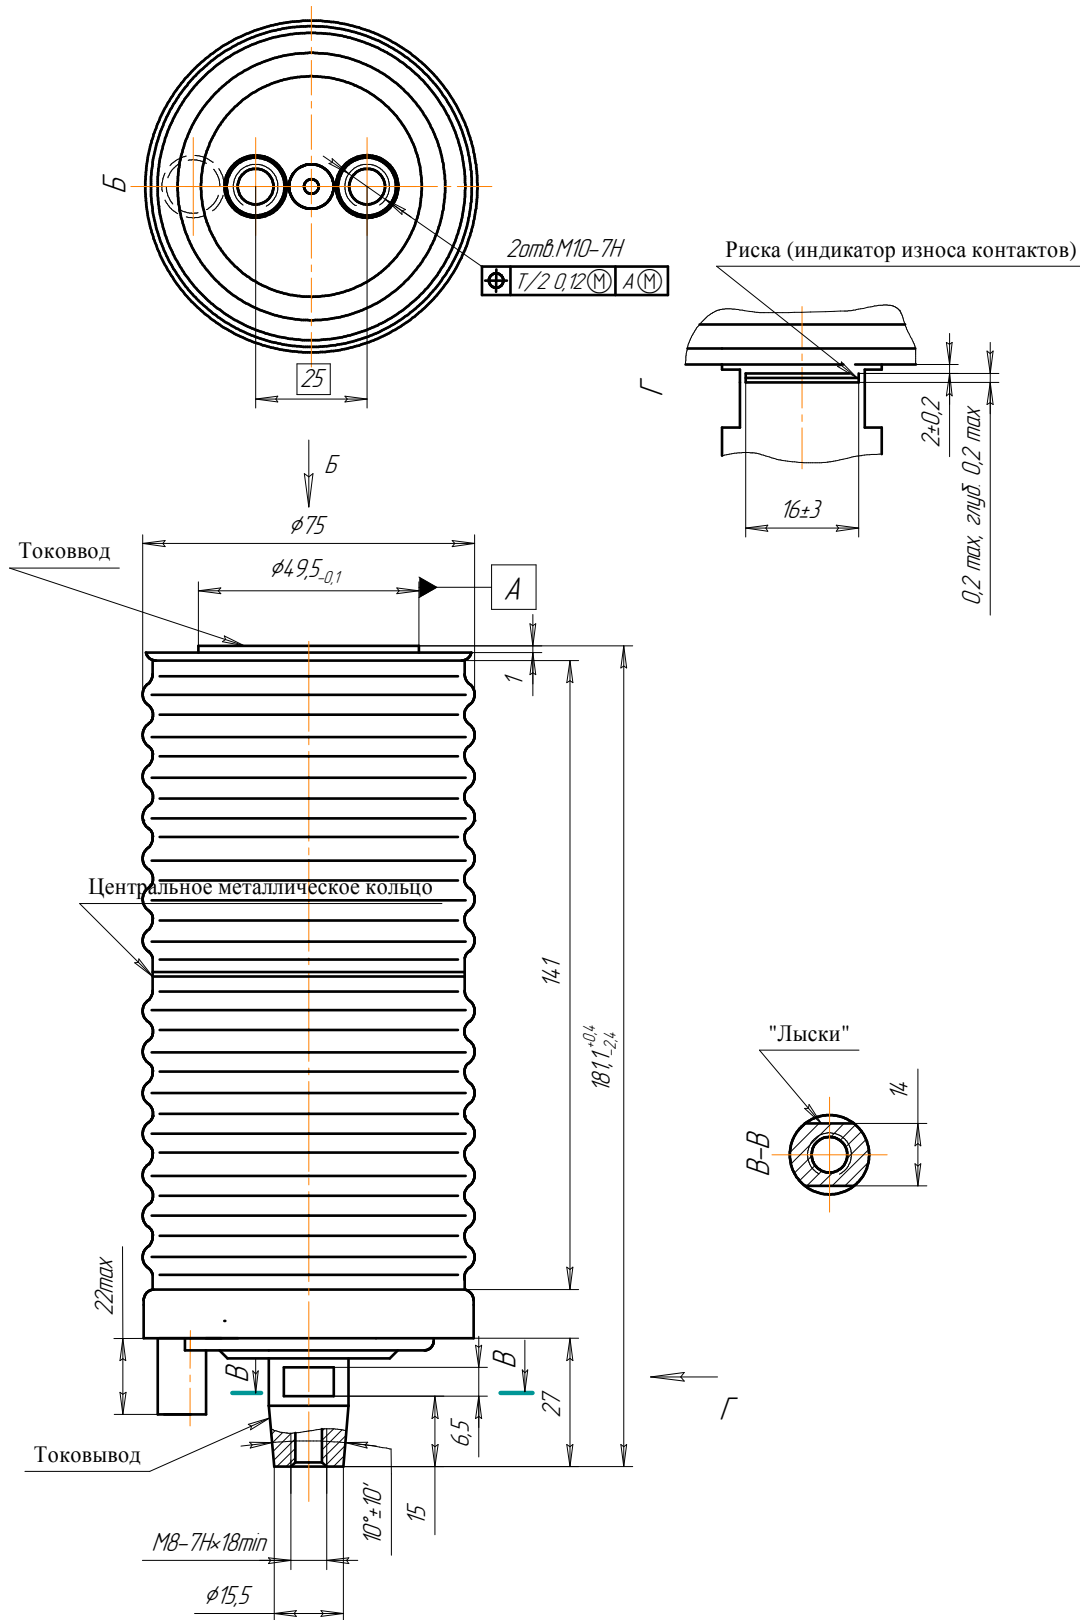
Габаритные, присоединительные и установочные размеры камеры типоисполнения КДВЗ-10-5/400 УХЛ2-1
